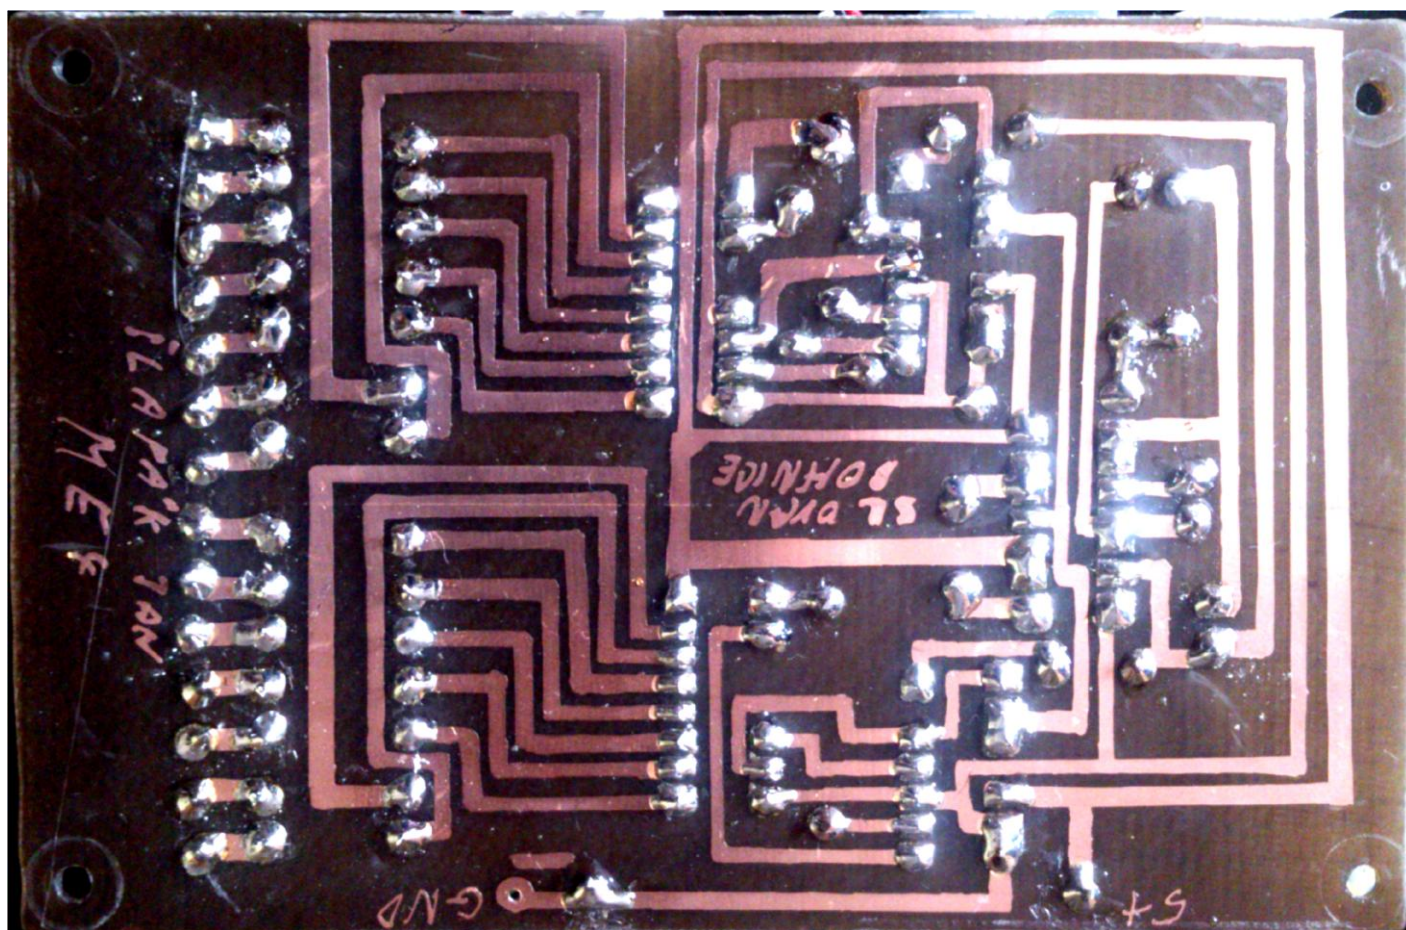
zapojení v boardu mirrored bez součástek)
